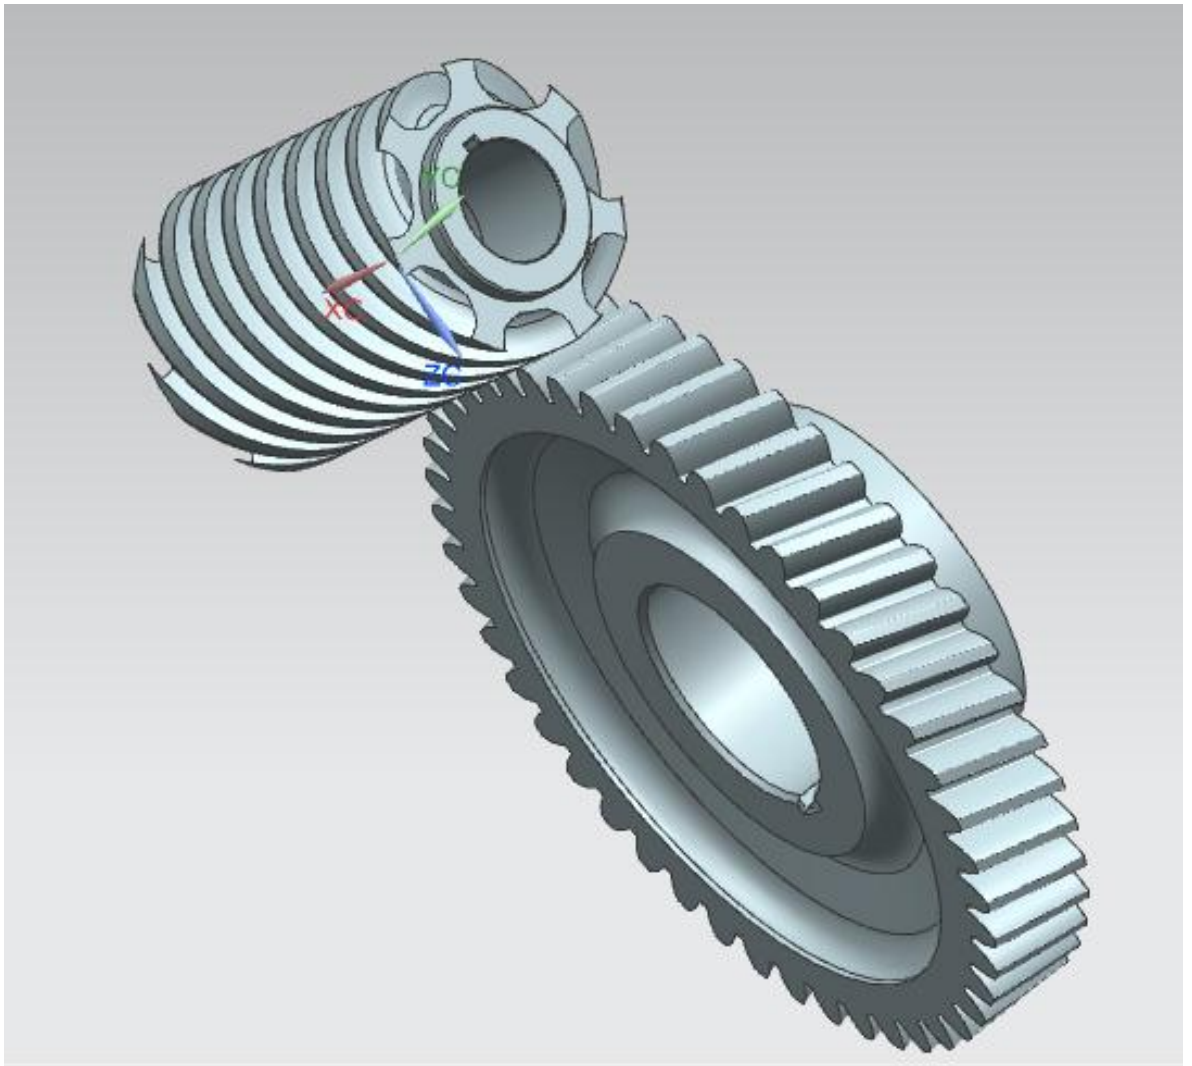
Визуализация наладки инструмента червячного типа со сплошными винтовыми режущими кромками на станке в модуле “Сборка” системы NX
